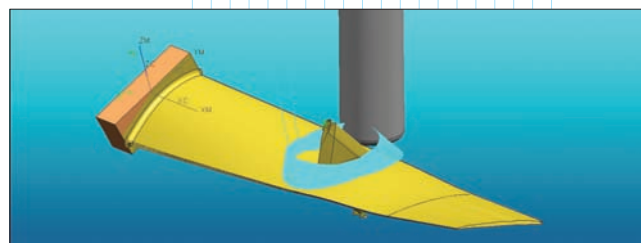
Черновая и полужистовая многокоординатная обработка полки лопатки торцевым инструментом
